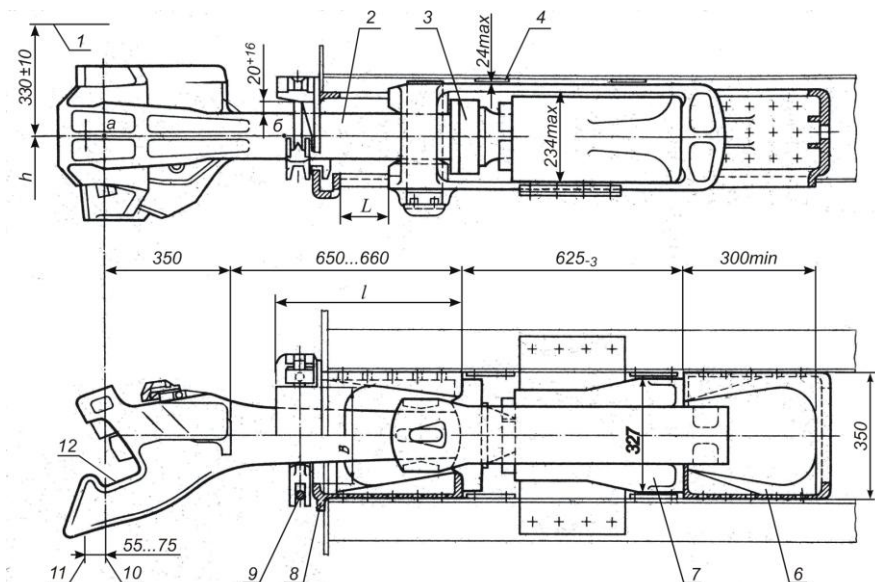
Основные установочные размеры автосцепного устройства:
